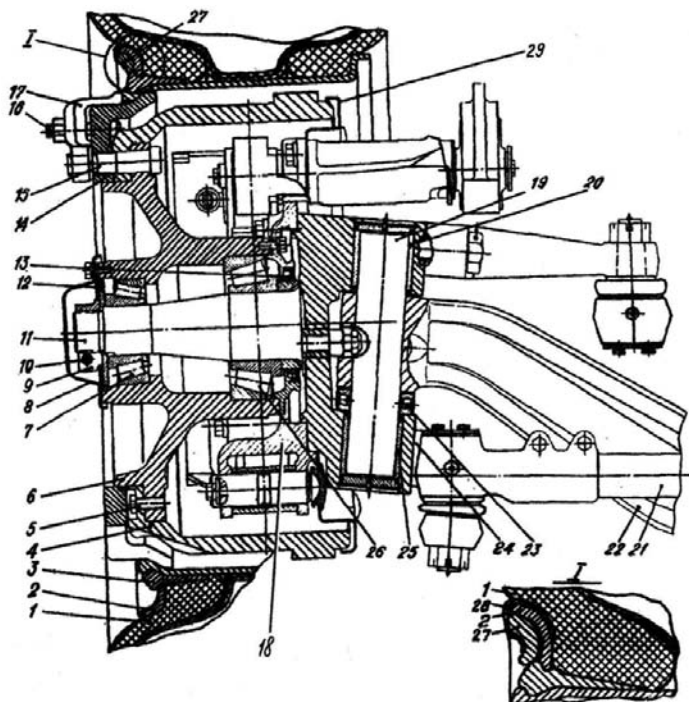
Передняя ось и ступица переднего колеса при установке бездисковых колес: 1 — колесо; 2 — кольцо бортовое; 3 — кольцо замочное; 4 — барабан тормозной; 5, 15, 16 — болты; 6 — ступица; 7, 23, 26 — подшипники; 8 — крышка; 9 — гайка; 10 — болт; 11 — кулак поворотный; 12 — шайба; 13 — сальник; 14 — диск; 17 — прижим; 18 — суппорт; 19 — шкворень; 20, 25 — втулки; 21 — тяга поперечная рулевая; 22 — балка передней оси; 24 — рычаг поперечной рулевой тяги; 27 — груз балансировочный; 28 — пружина; 29 — щит тормоза
